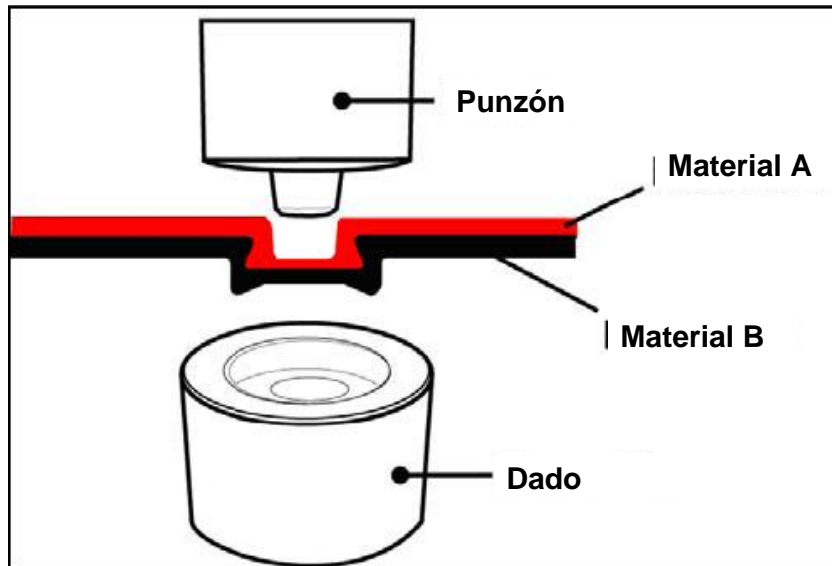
Esquema que muestra el mecanismo de engrapado [6].
